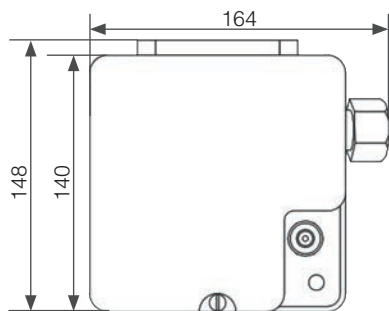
Блок контактный реагирующий БКР1 и БКР2 (вид сверху)
